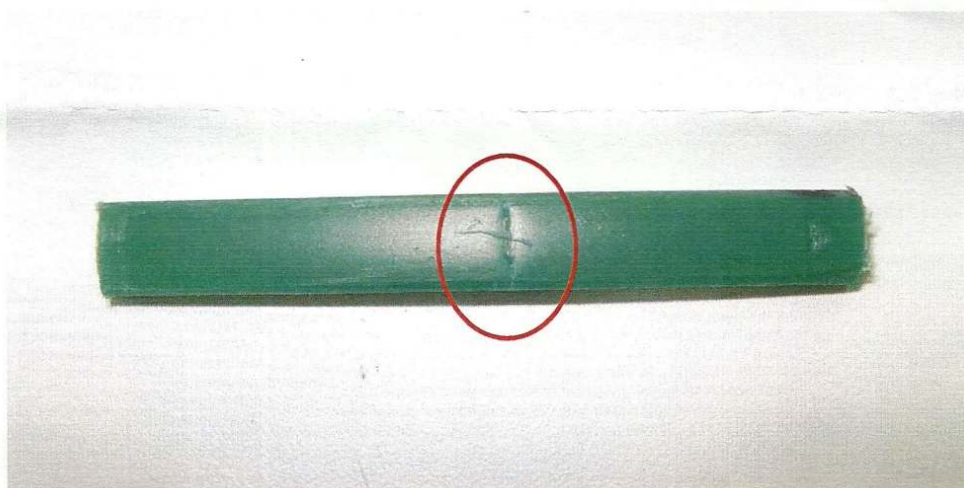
Corpo de prova nº 3 após aplicação do impacto. Verificada ocorrência de fissura após a realização do impacto.
